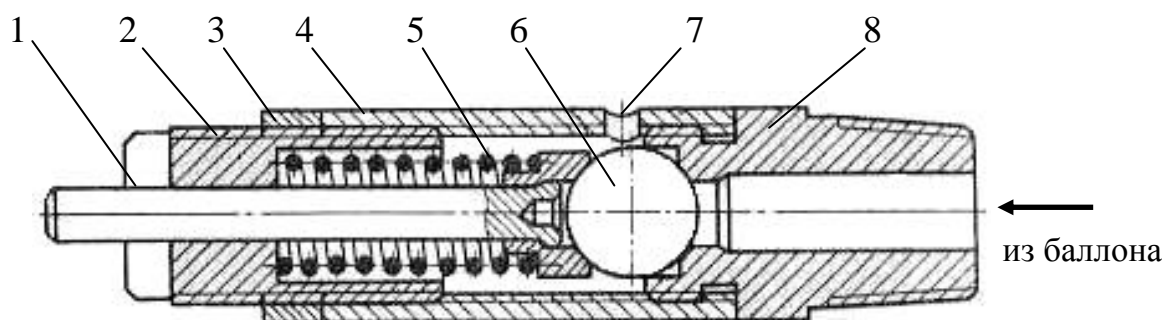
Предохранительный клапан: 1 – упорный шток; 2 – регулировочный винт; 3 – контргайка; 4 – корпус; 5 – пружина; 6 – шарик; 7 – атмосферное отверстие; 8 – седло клапана
